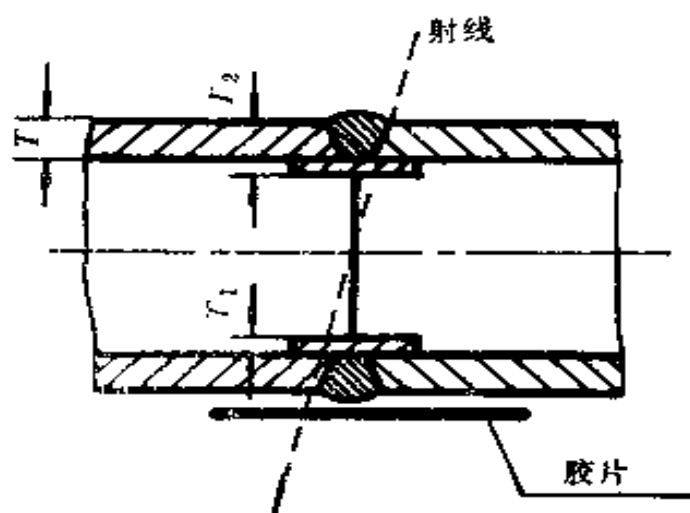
带垫板的对接焊缝透照
